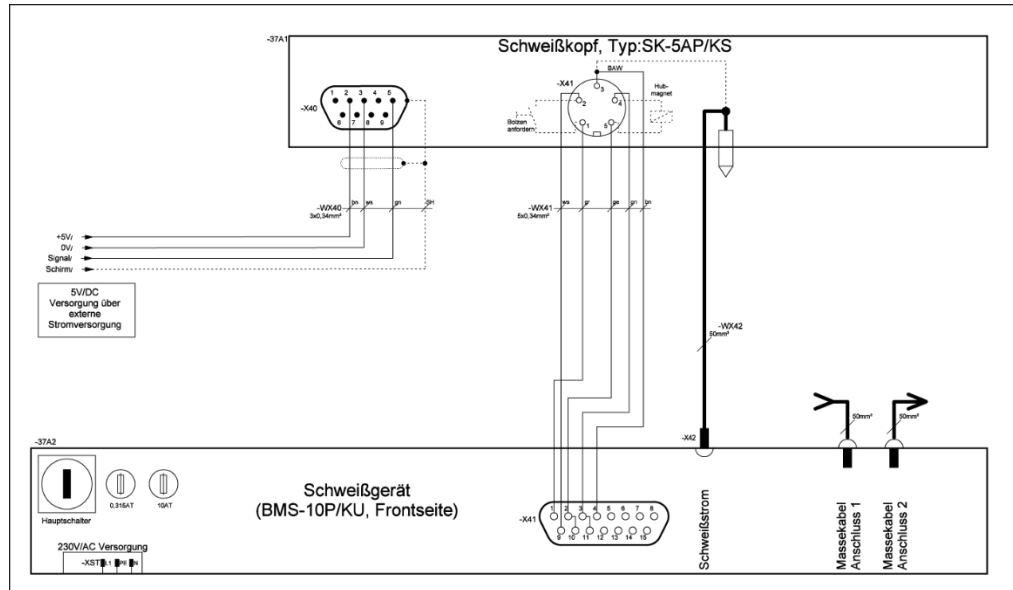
Anschlussschema Bolzenschweißkopf mit BMS-10P
